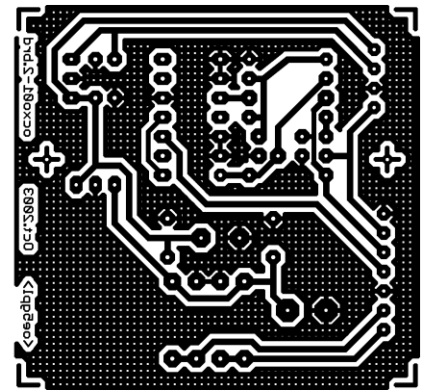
Leiterplatten-Layout Stromversorgung & Teiler
